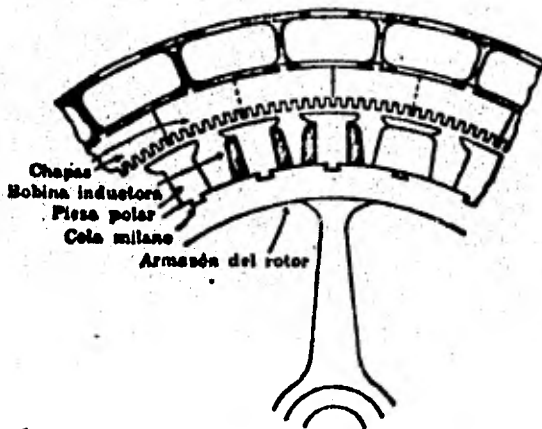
Sección transversal de un alternador accionado por máquina de vapor.
